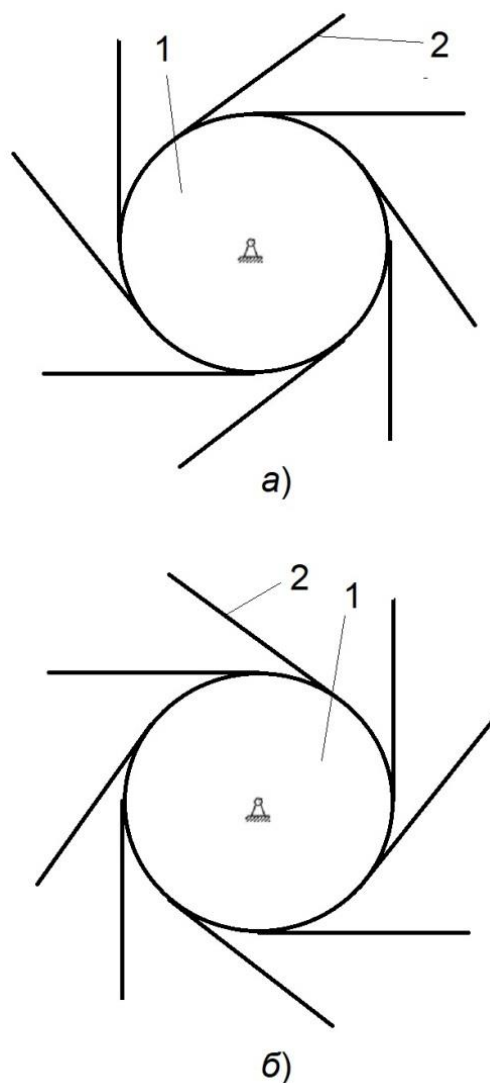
Условная схема сечения смесительного барабана с упругими лопатками в различных ярусах: а – ярус А; б – ярус В; 1 – цилиндрический барабан; 2 – лопатка
